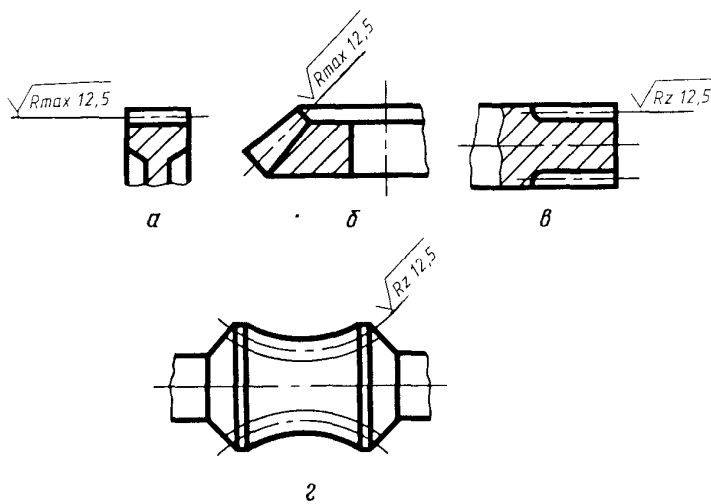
Обозначение шероховатости на зубчатых поверхностях
